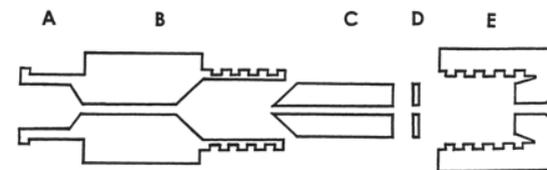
Принципиальная схема конектора. А – люэровский разъем, В – корпус с резьбой, С – резиновая прокладка, D – металлическая прокладка, E – фиксатор катетера.
